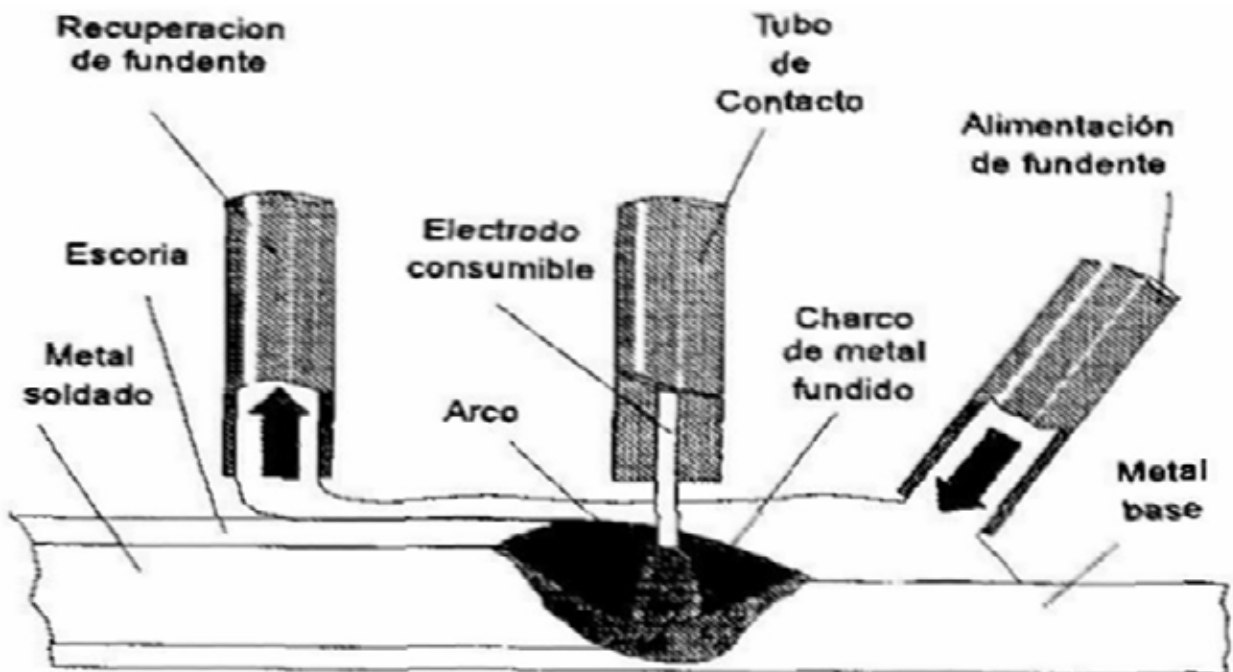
Soldadura de Arco Eléctrico Sumergido (SAW)
